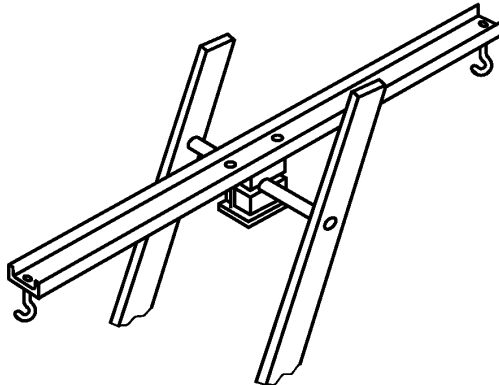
Приспособление для испытания ступеньки на кручение
